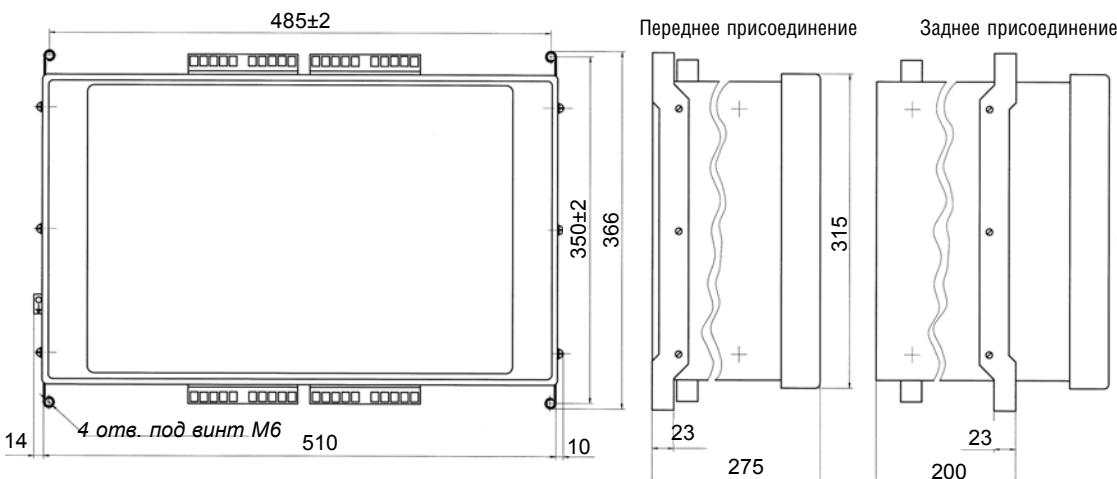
Габаритные, установочные размеры блока типа БЭ 1104.
